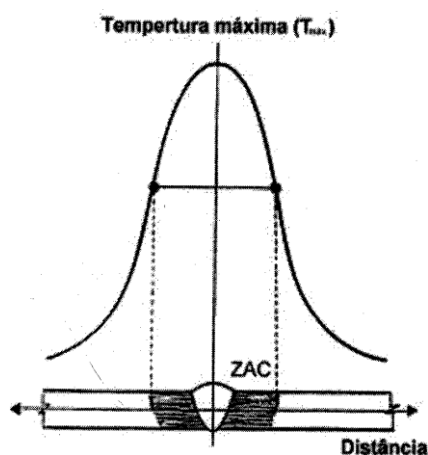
Repartição térmica de uma junta soldada [45].
